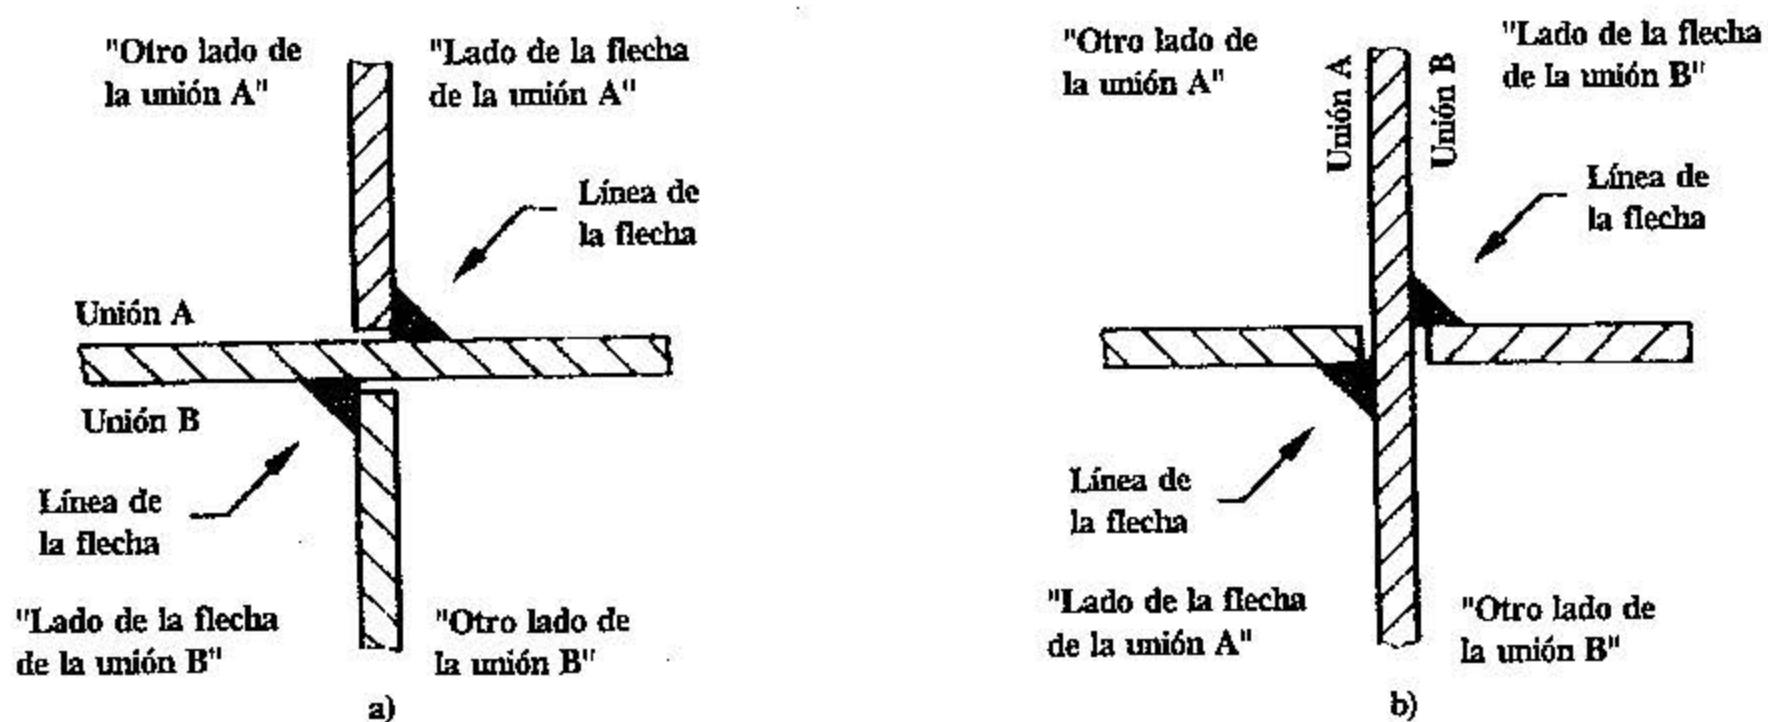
Unión cruciforme con dos soldaduras en ángulo
